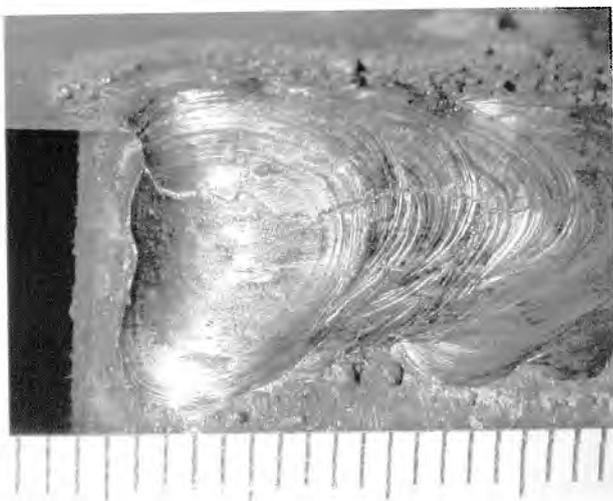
Разветвленная трещина нахлесточного сварного соединения. Детальный вид
